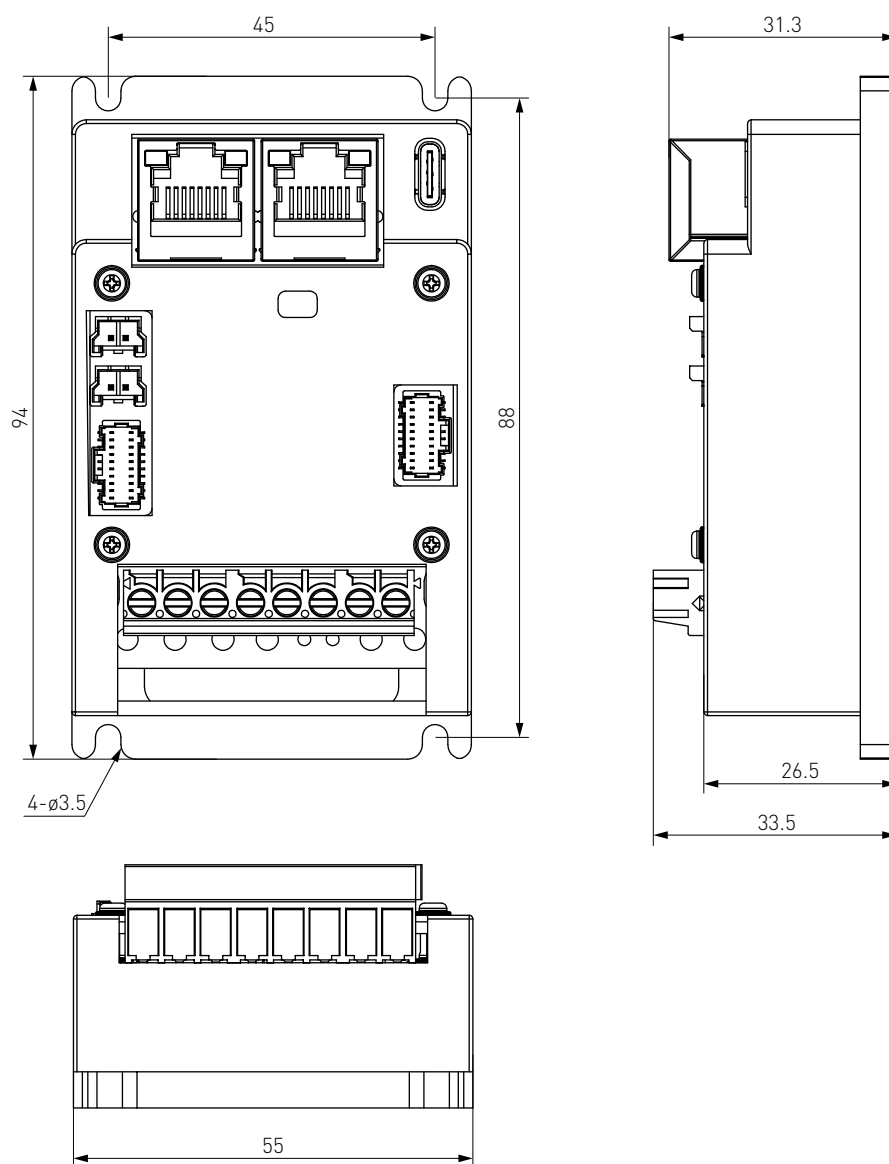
Габаритный чертеж серводрайверов ELD3-EC7010/7020BH.
